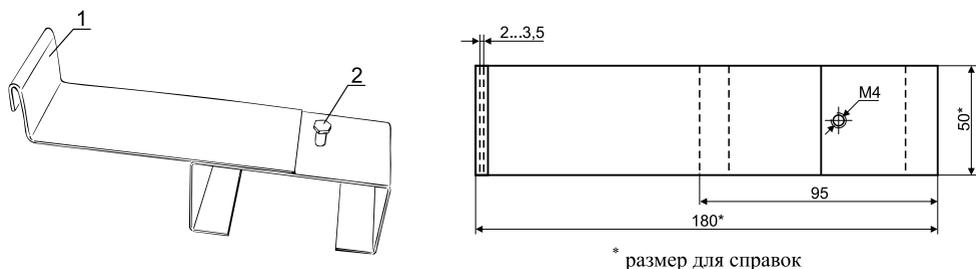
Внешний вид и габаритные размеры кронштейна крепления «БОС» к МПП «Гарант-12»
